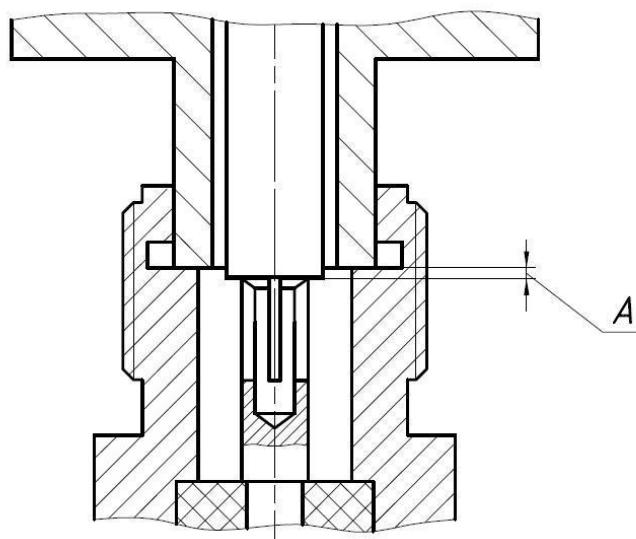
Проверка размера «A» соединителя «розетка»
